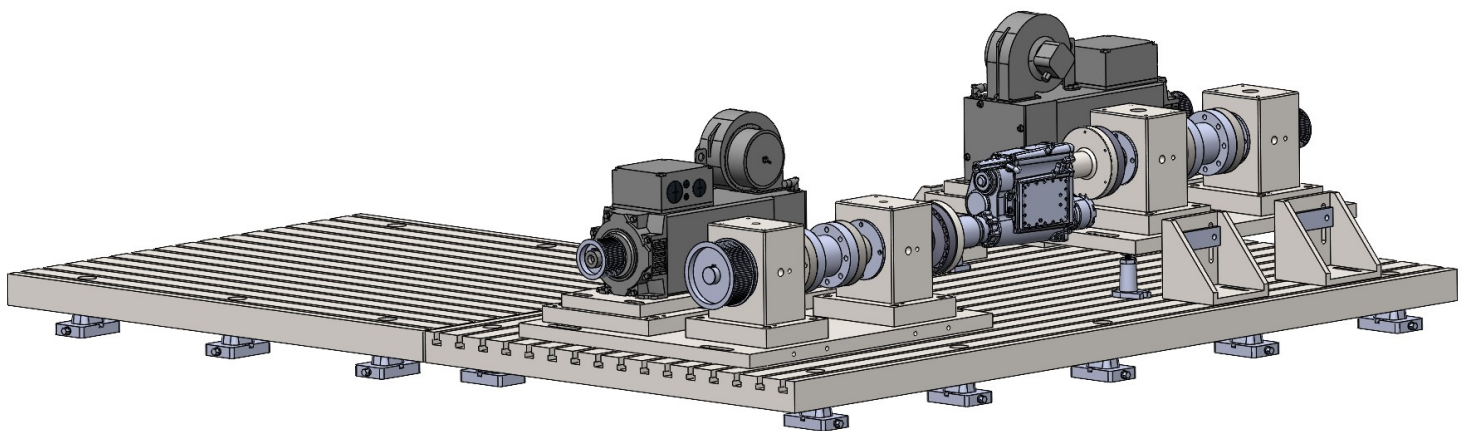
Zusammenbauansicht 1 Prüfstand- Komplet
